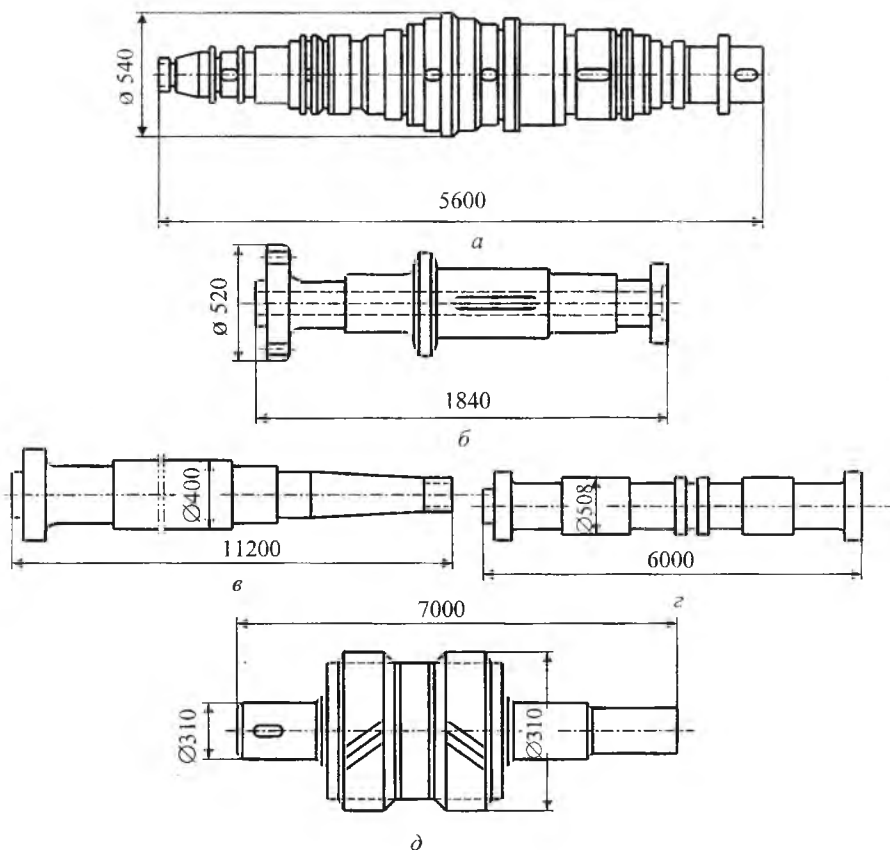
Типы валов: *a* – многоступенчатые; *б* – валы полые или имеющие центральные глубокие отверстия; *в* – валы с коническими поверхностями и резьбой; *г* – валы фланцевые; *д* – валы шестерни
